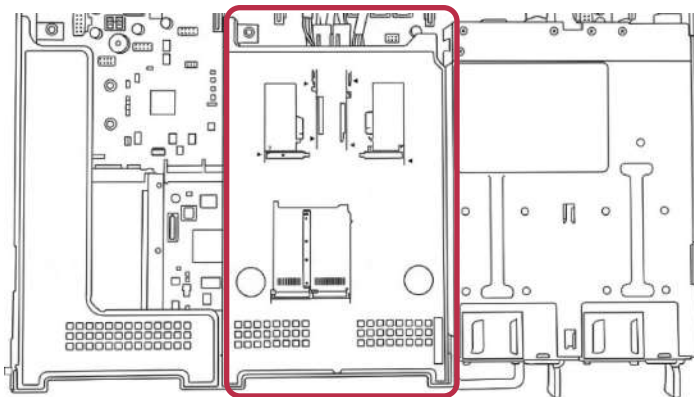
Установка корзины Riser 2 (Riser 3) в корпус
